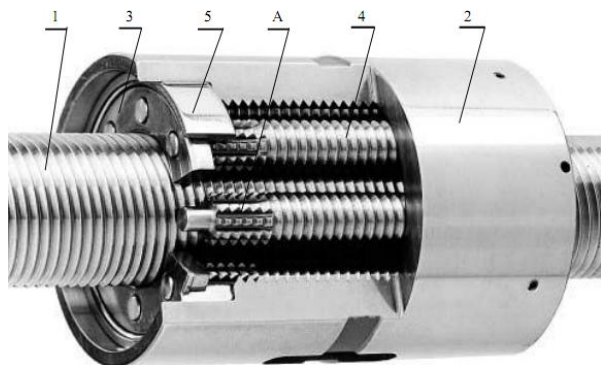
ПРВМ с зазорами между резьбовыми деталями
